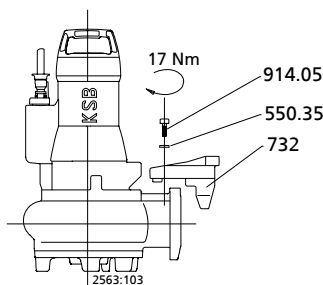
Установка крепления при тросовых направляющих, 1 направляющей штанге и хомуте.
